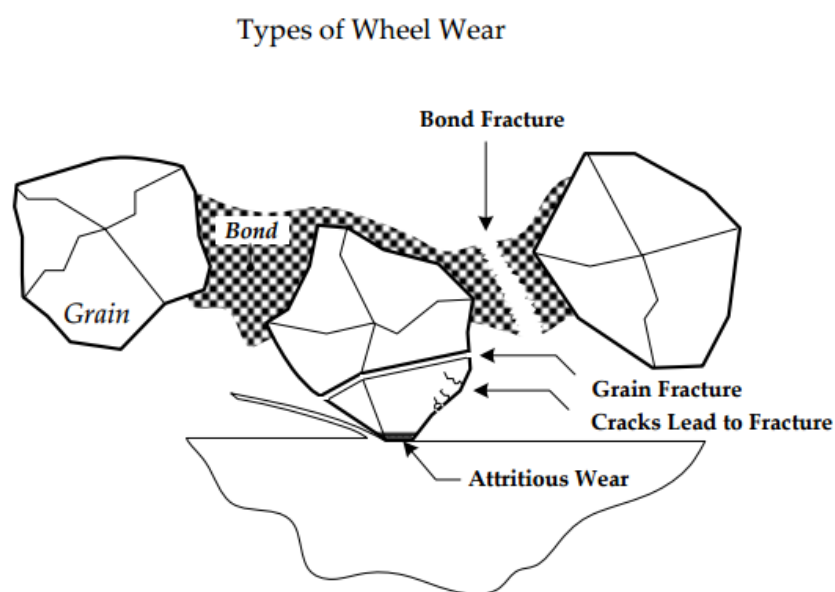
Механізми зношування шліфувального круга [23, 25]
